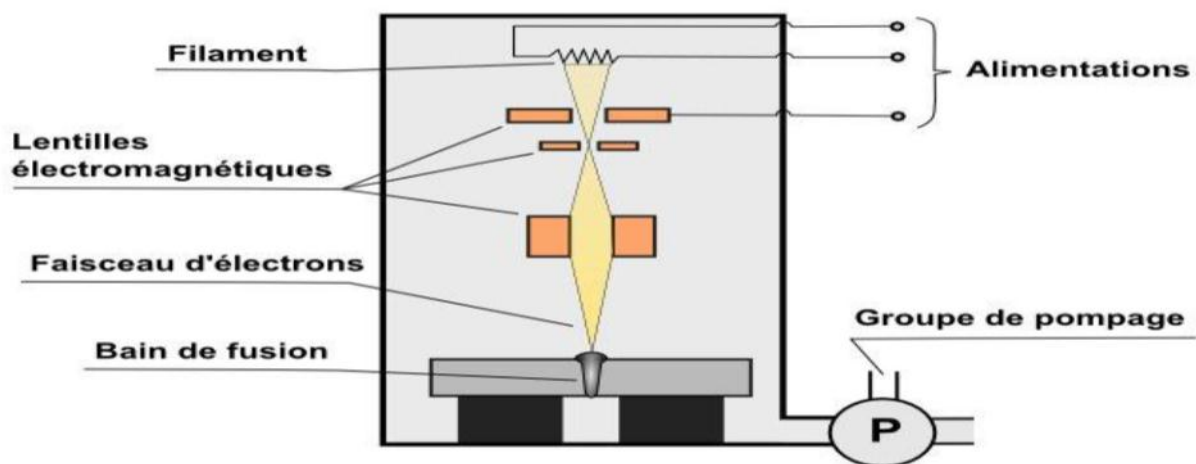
Soudage par faisceau d'électron [22].
